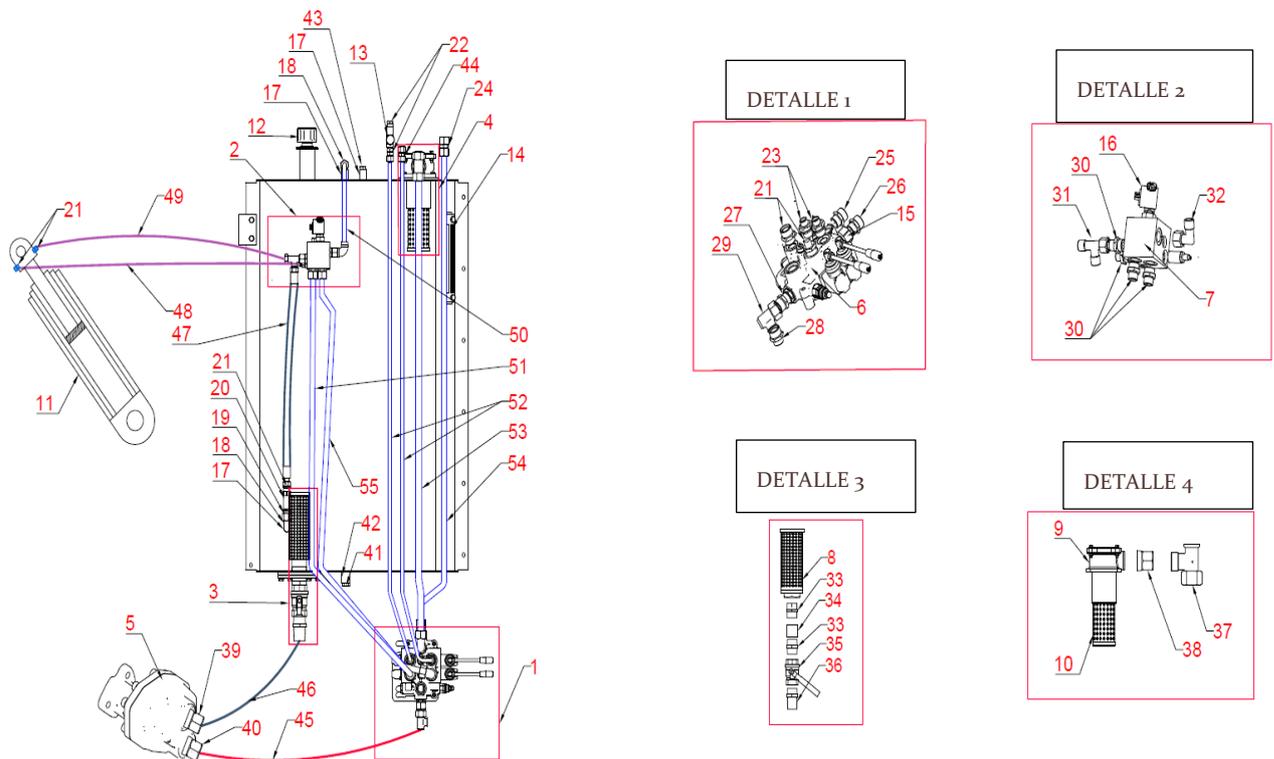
Presentación del Montaje Hidráulica del Tanque de Aceite
